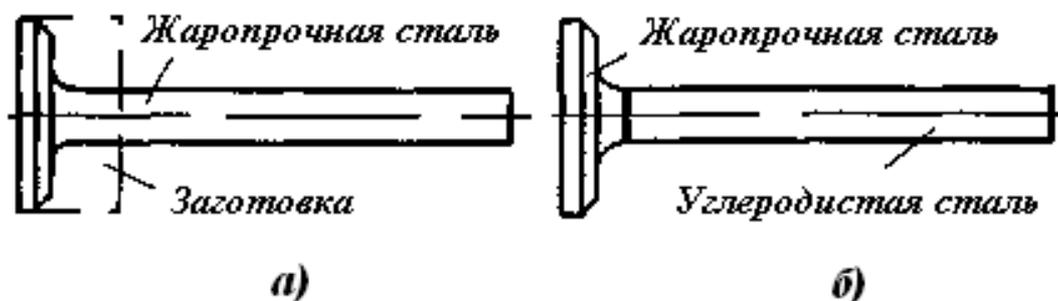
Изготовление клапанов по старой технологии (а) и с применением сварки трением (б)
